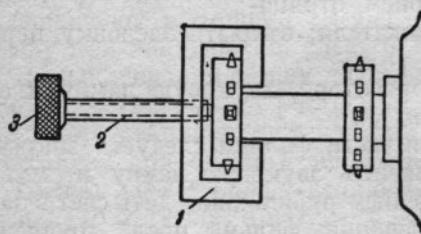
Приспособление для снятия зубчатого барабана с вала кинопроектора
